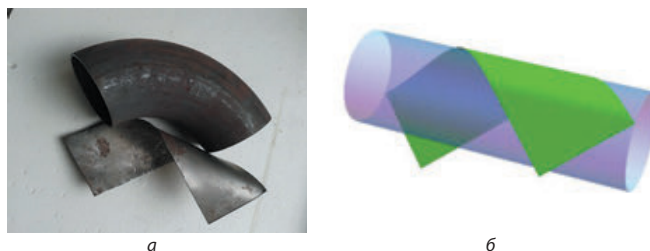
Детали заводского опытного образца отвода: а – заготовки изделия; б – схема профилирования лопатки
